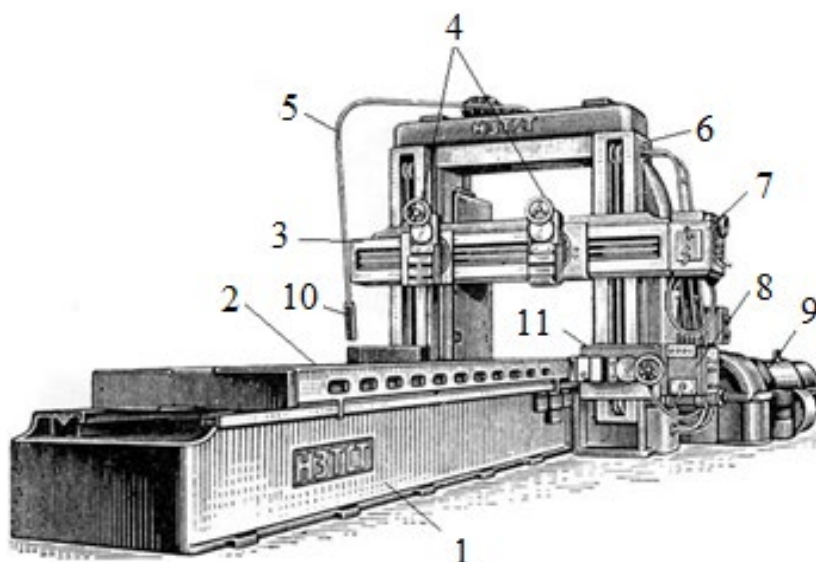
Загальний вигляд поздовжньо-стругального верстата
